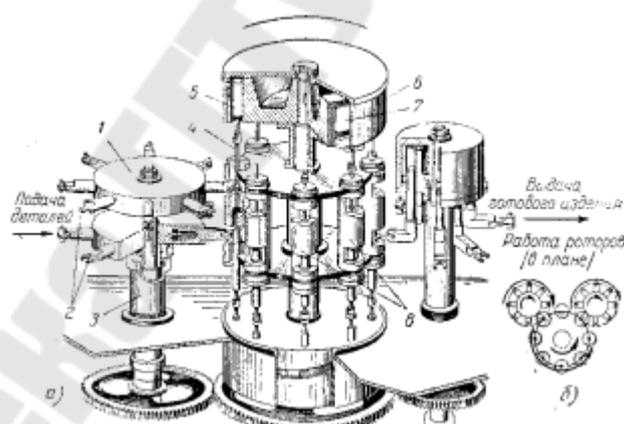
Типовой ротор для сборки двух элементов и обслуживающие его транспортные роторы: а – конструкция ротора; б – схема работы роторов в плане: 1 – диски; 2 – клещевые несущие органы; 3 – стакан; 4 – рабочий инструмент-пуансон; 5 – ползун; 6 – барабан; 7 – неподвижный пазовый копиер; 8 – блоки рабочего инструмента
